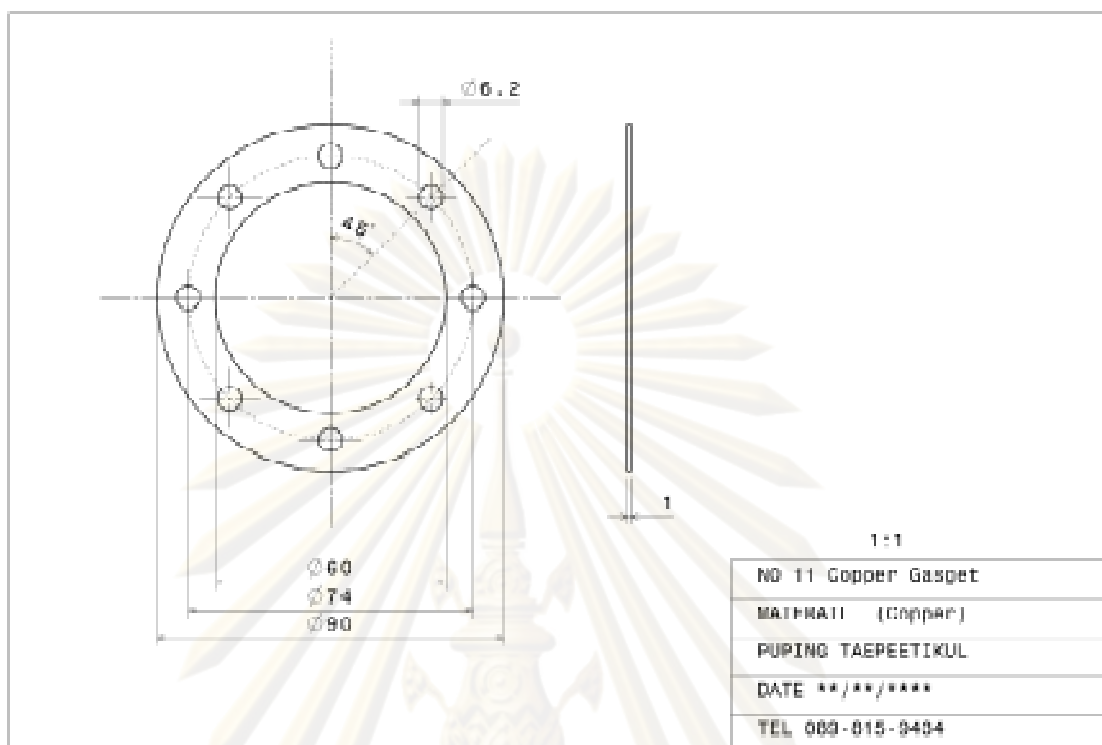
แบบ Drawing (Geometrical detail) ของ MCHP
